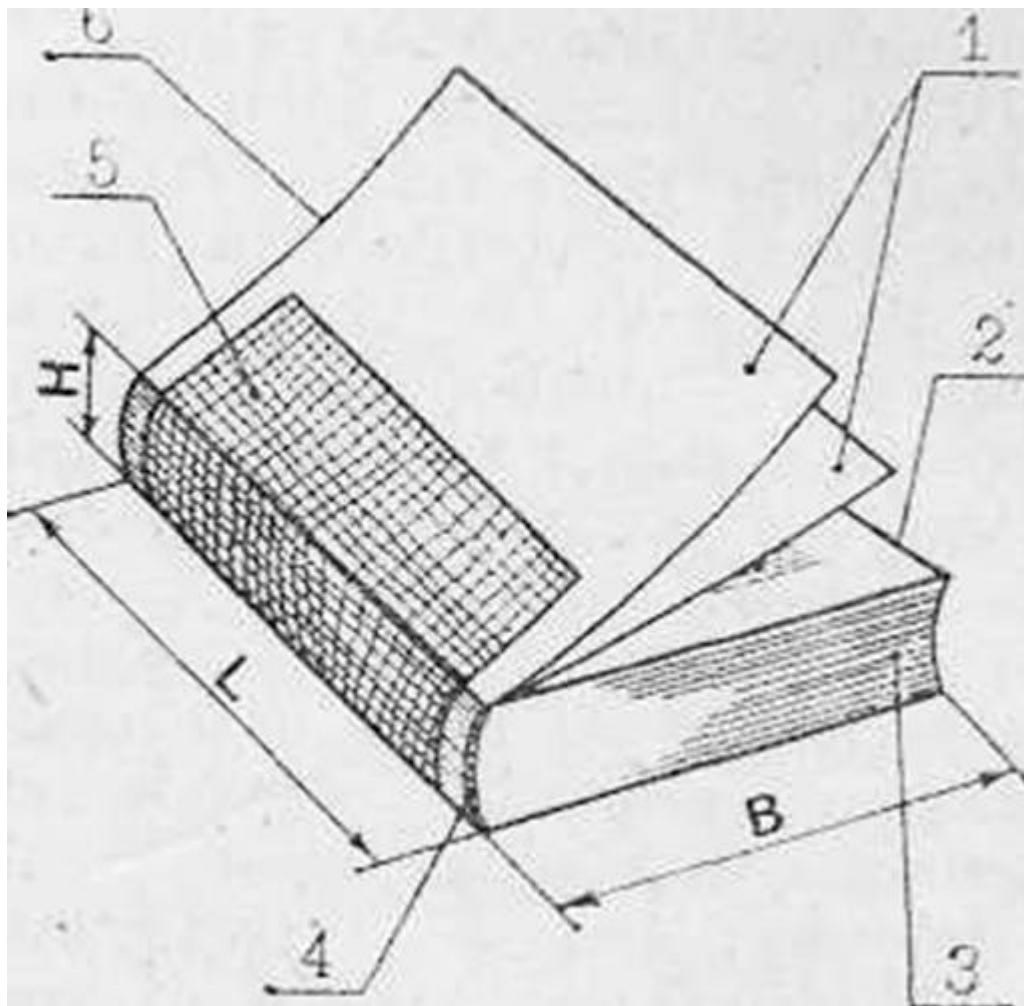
Книжный блок: 1 – форзац; 2 – передний обрез блока; 3 – нижний обрез блока; 4 – каптал; 5 – марля; 6 – верхний обрез блока; B – ширина блока; L – длина блока (высота); H – толщина блока
